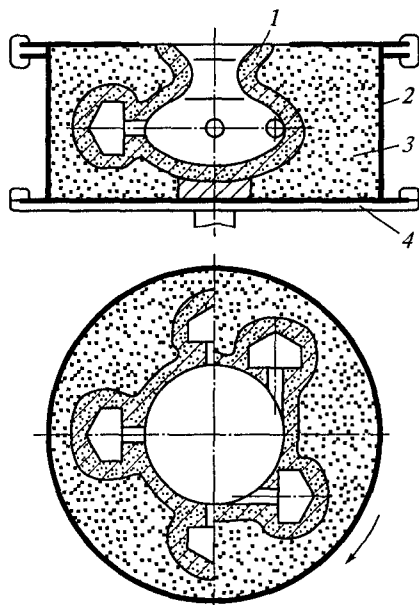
Форма для центробежной отливки, собранная из стержней
